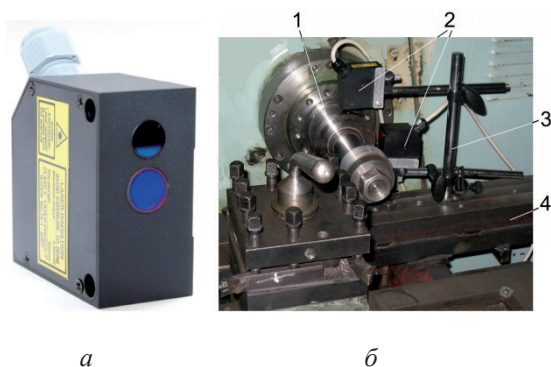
Триангуляційний лазерний датчик (а) та загальний вигляд (б) схеми закріплення: 1 – прецизійна оправка; 2 – датчики; 3 – стійка; 4 – плита
